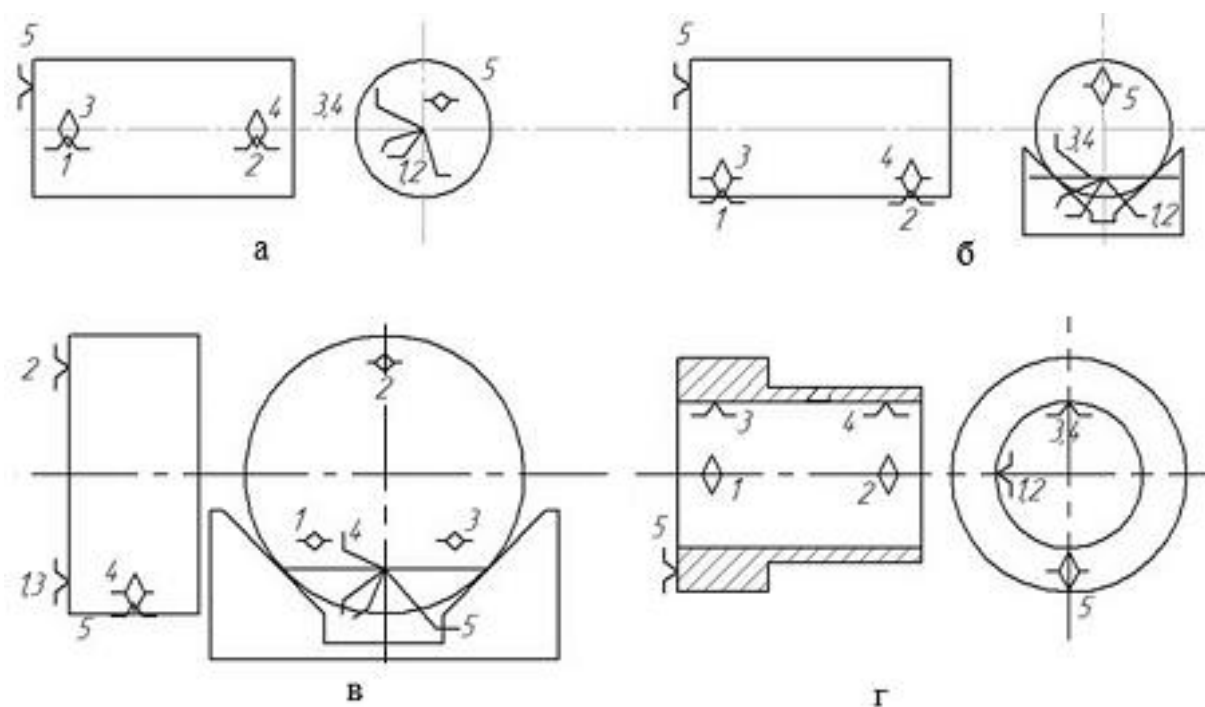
Основні схеми базування різних заготовок за довгою циліндричною поверхнею при її установці в трьохкулачковому самоцентруючому патроні (а), в призмі (б, в) та на оправці (г)
